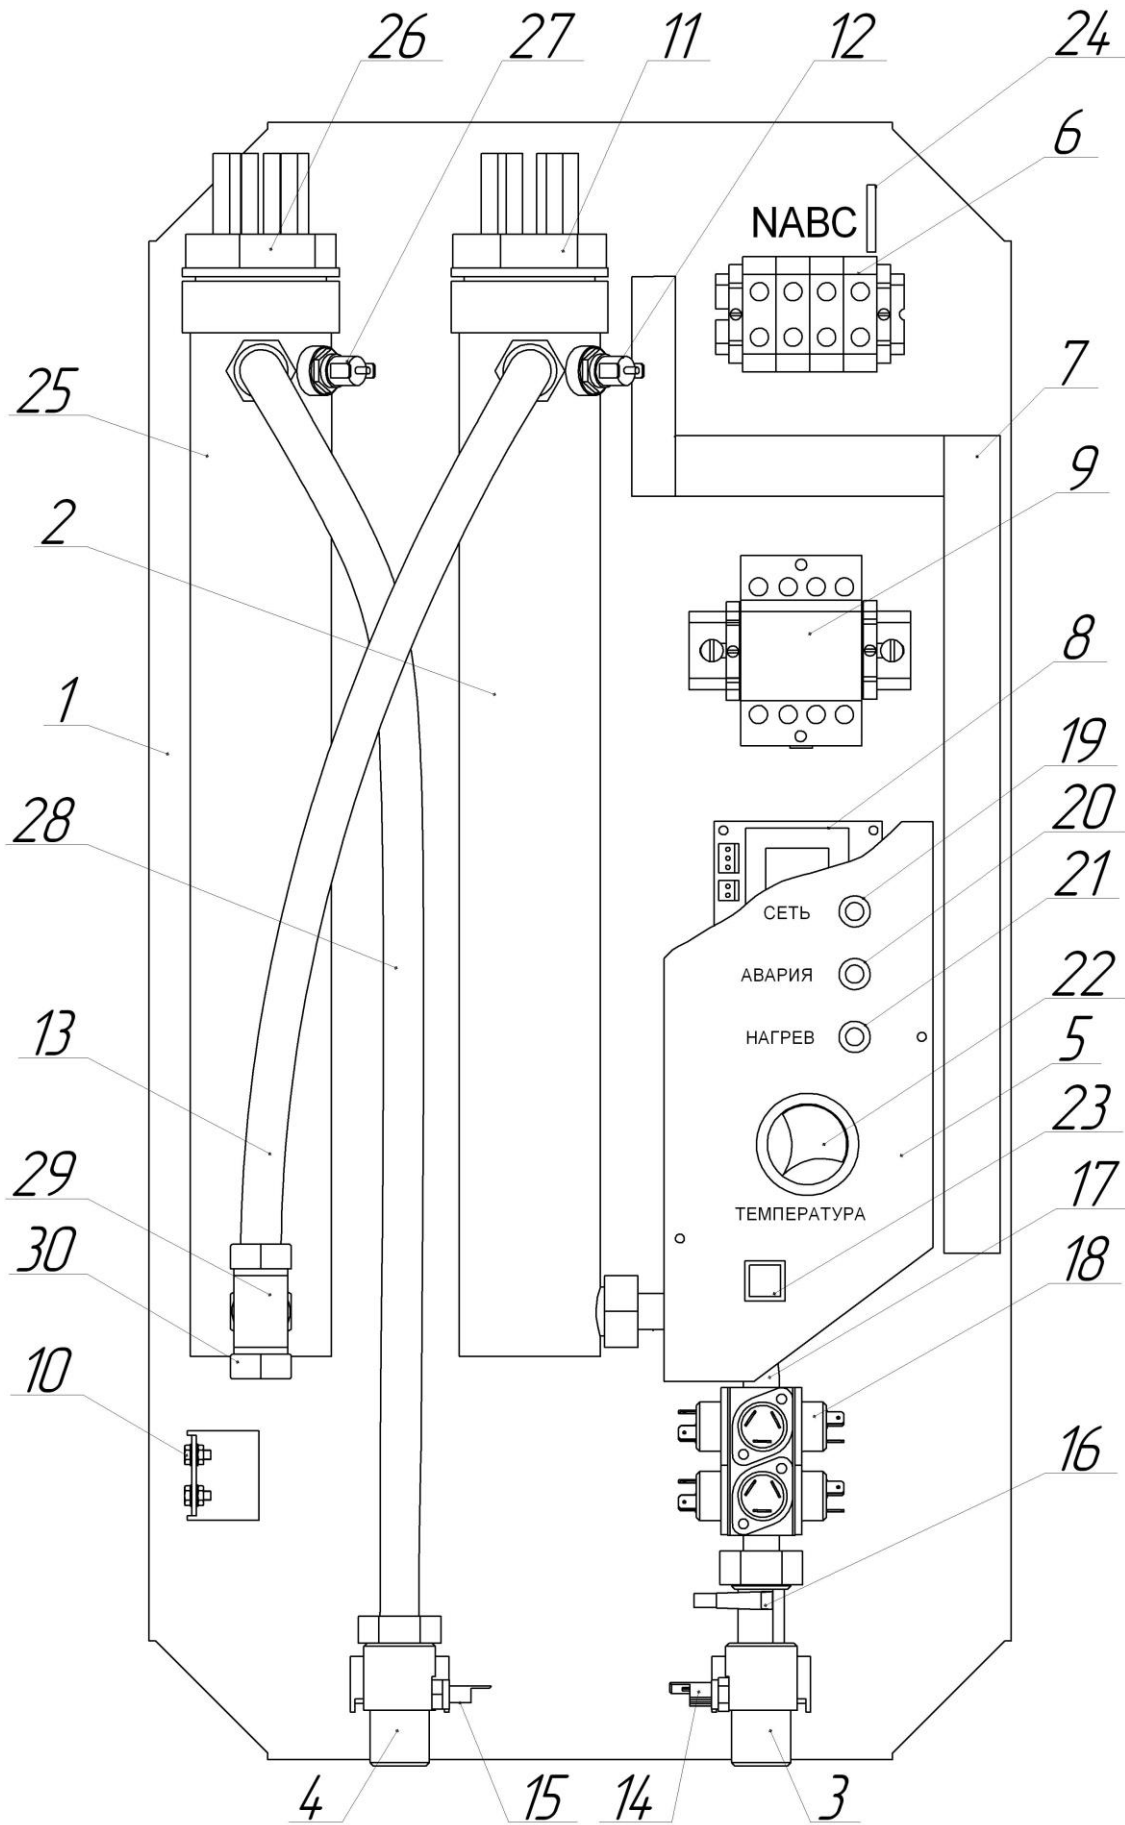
Внешний вид прибора ПВС-01-18 (24, 30) (со снятым кожухом)
